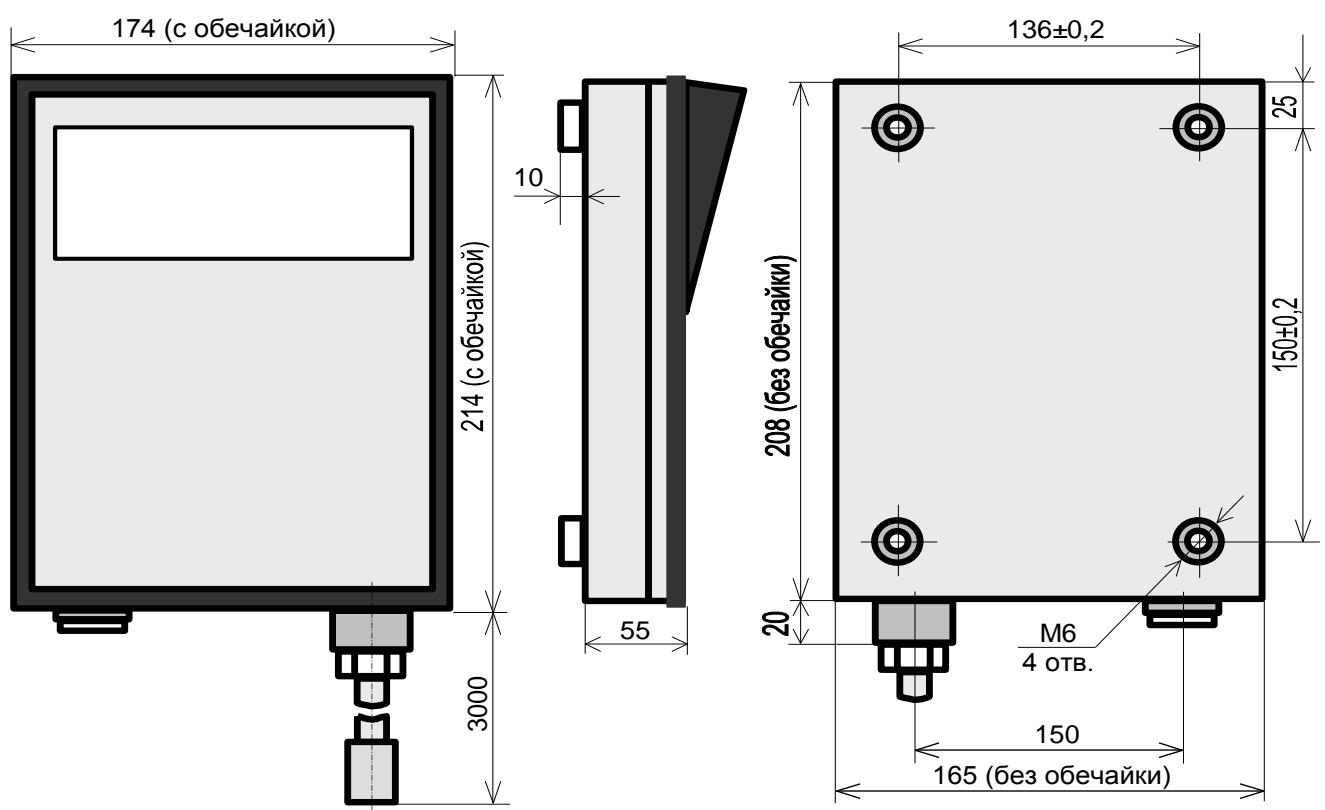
Габаритные и присоединительные размеры БОИ
